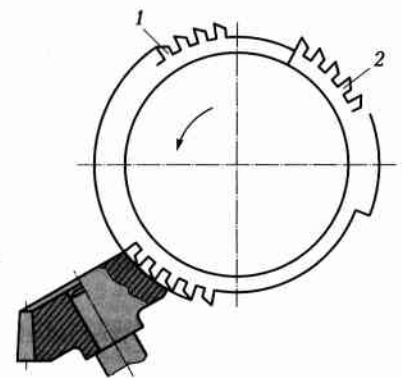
Схема нарезания конического колеса круговой протяжкой
